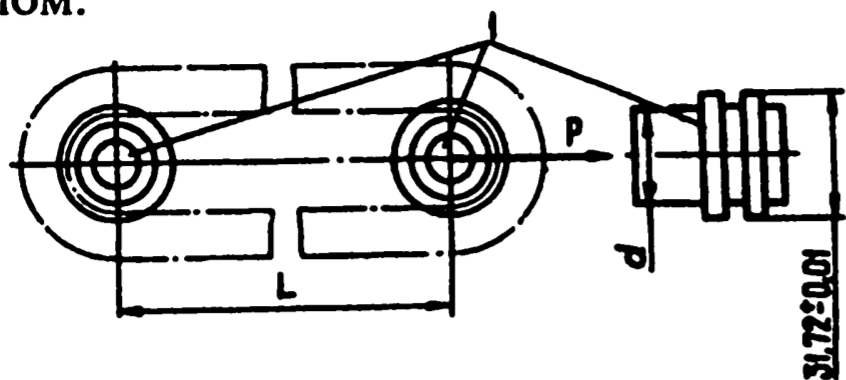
Схема проверки износа (вытяжки) цепи: 1 - ролики
